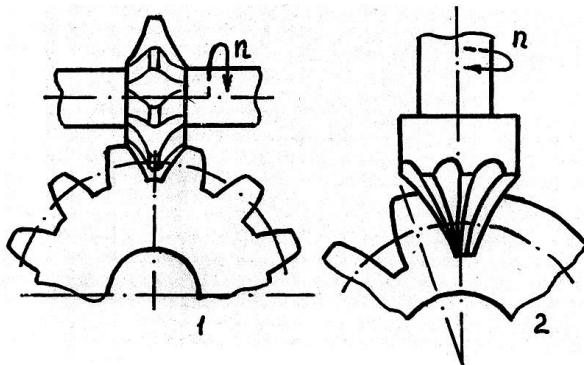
Схема фрезерування зубців за методом копіювання:
